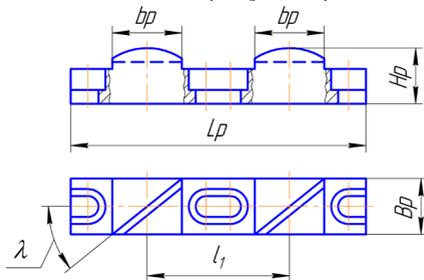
Конструкция резца-зуба развёртки со двоянными безвершинными зубьями
